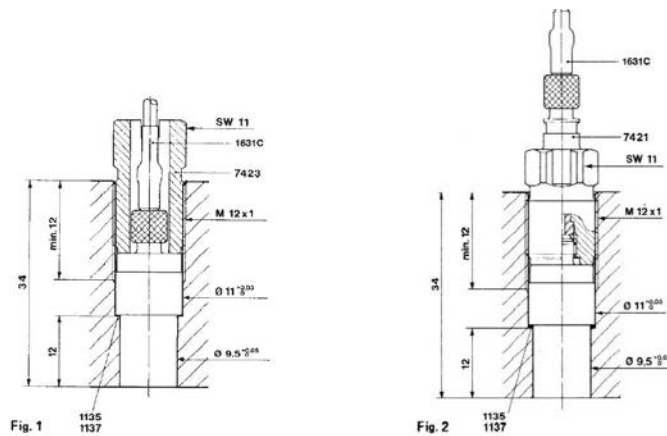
Montaje de los sensores de presión del tipo “flush-mounting”.
